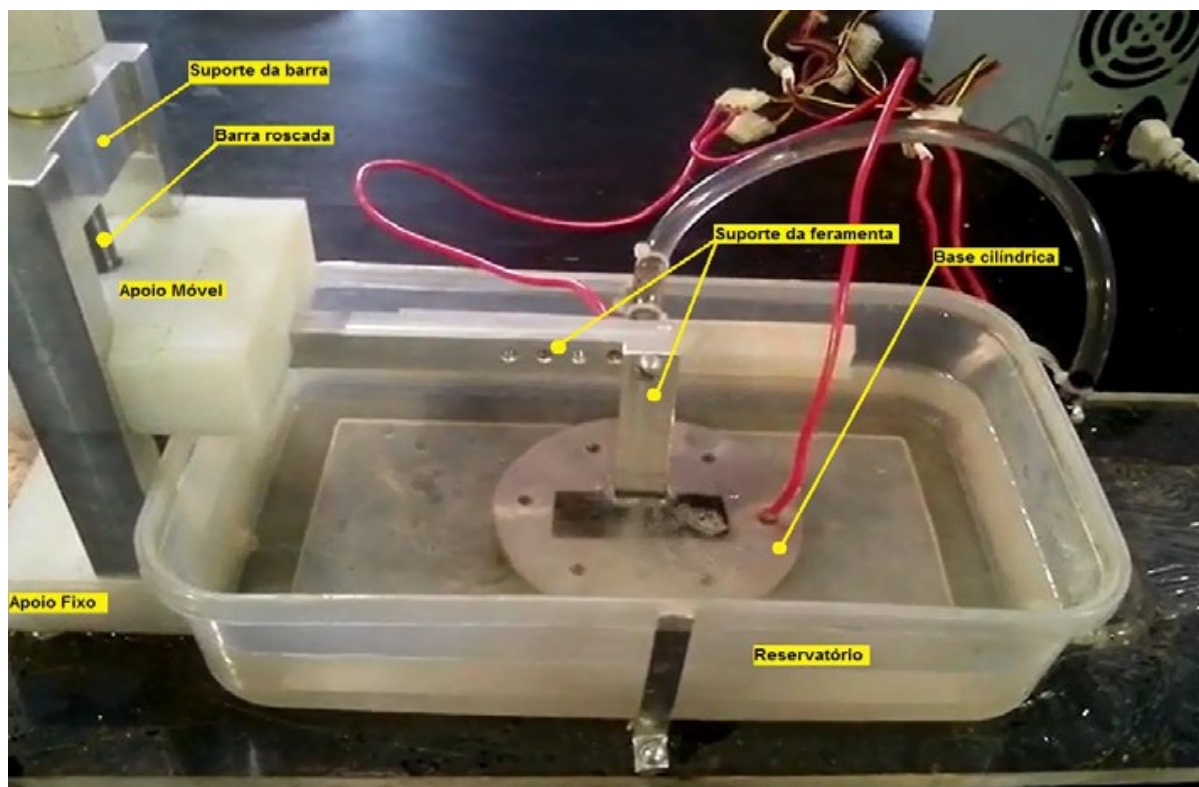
Protótipo da máquina de usinagem eletroquímica
